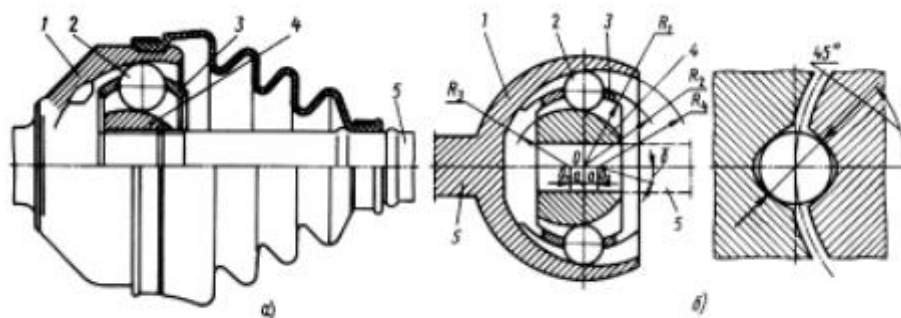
Шестишариковый карданный шарнир (типа “Бирфильд”): а – карданный шарнир; б – схемы карданного шарнира; 1 – корпус; 2 – шарики; 3 – сепаратор; 4 – кулак; 5 – вал
